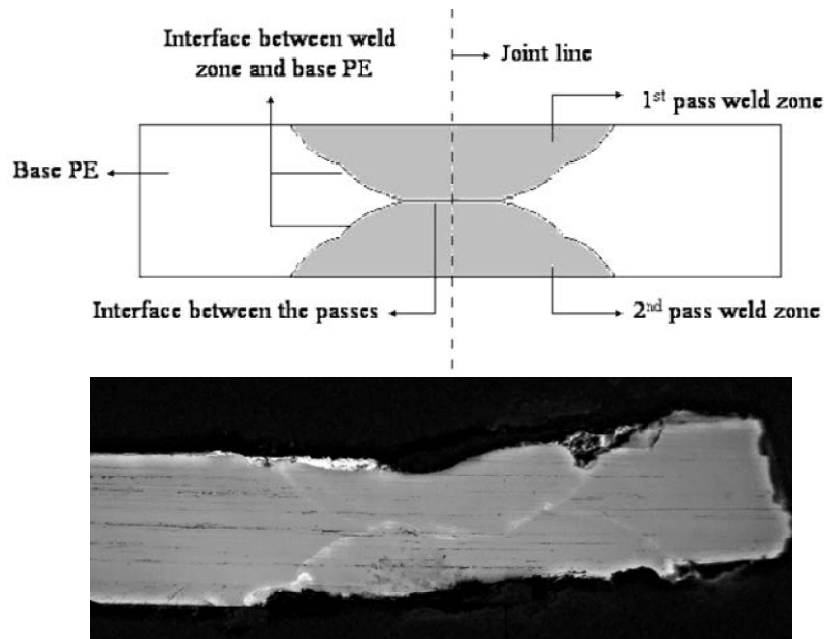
Schweißen von PE mittels beidseitigem FSW[24 S. 3315]
